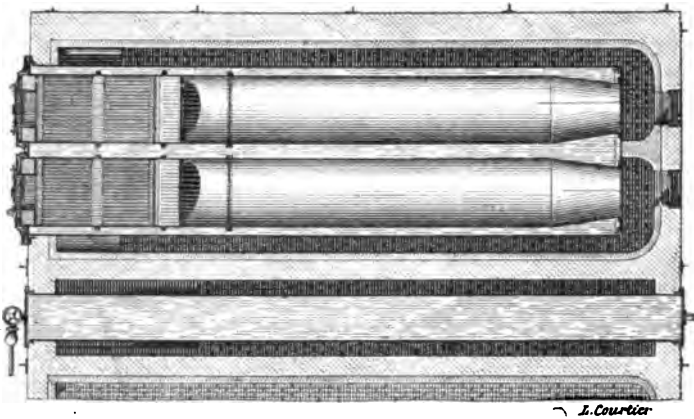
Chaudière de Lancastre (coupe horizontale).
